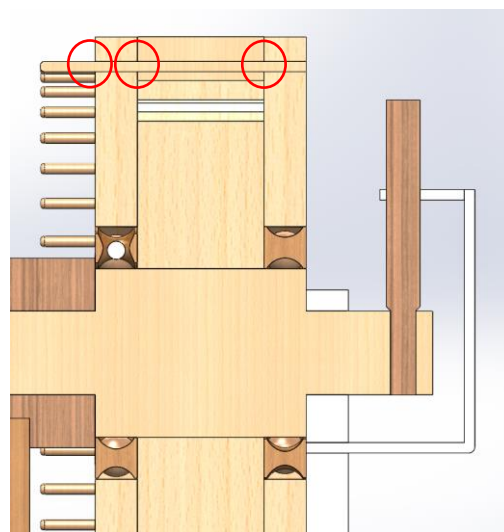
Rodamiento/Cojinete de bolas (Códice de Madrid I, f.0020v (detalle))
